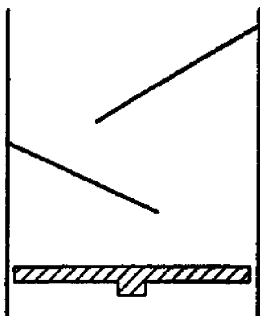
а – Загрузочное устройство с направляющими пластинами
